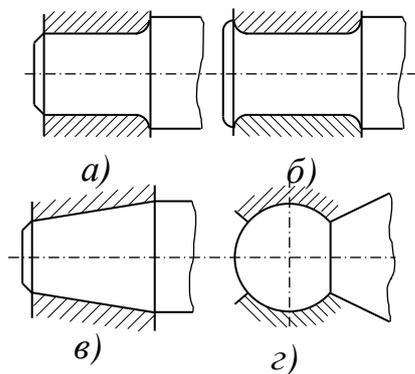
Основные типы цапф валов под подшипники скольжения
